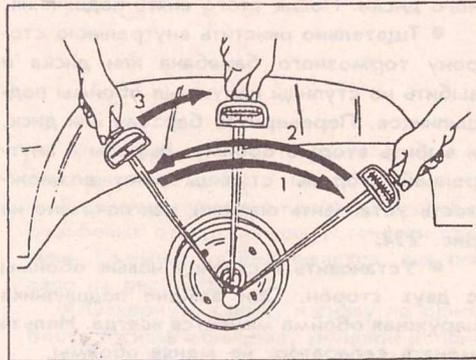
Три этапа регулировки подшипников заднего колеса.
